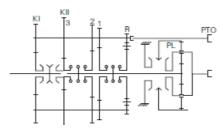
Схема силового потока в коробке передач ZF-AS Tronic с двумя промвалами
